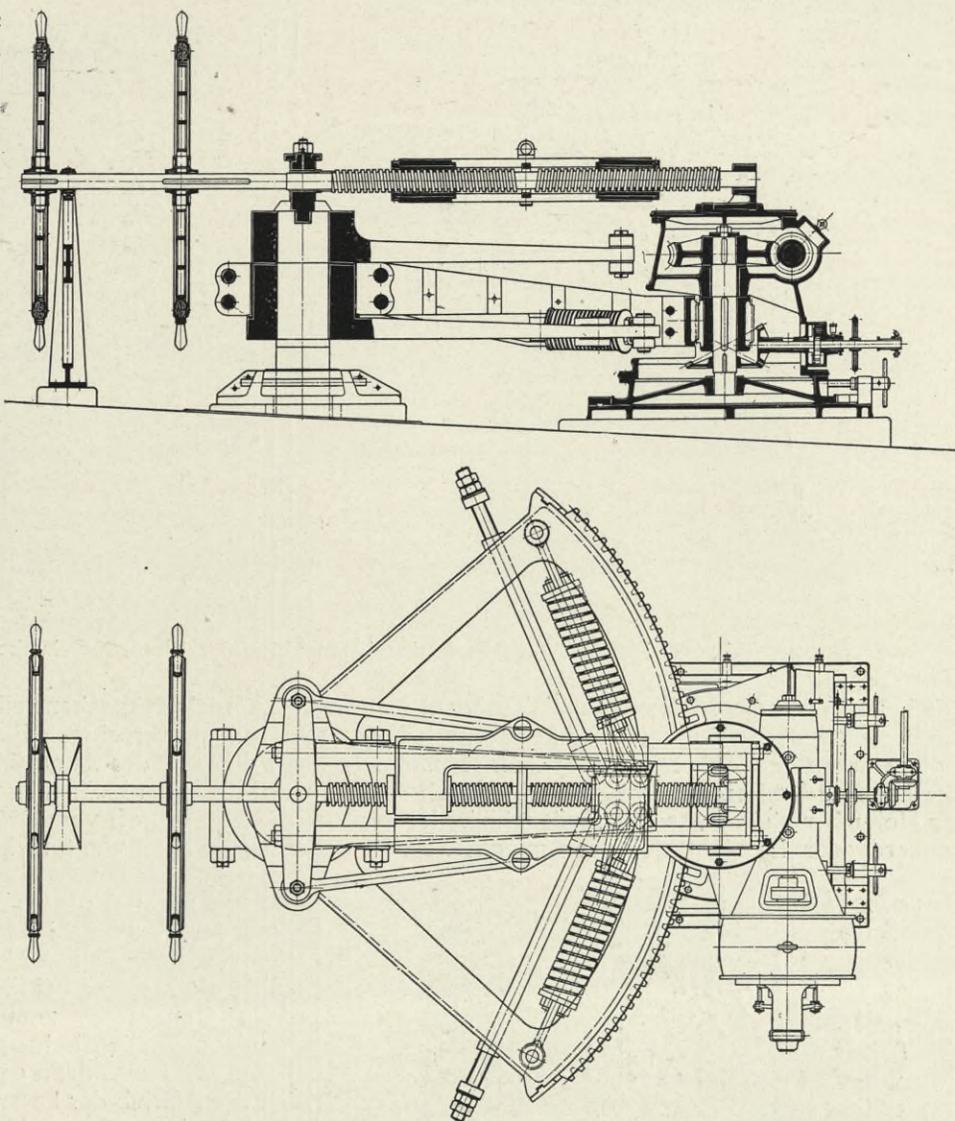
Rudermaschine der Atlas-Werke A.-G., Bremen
